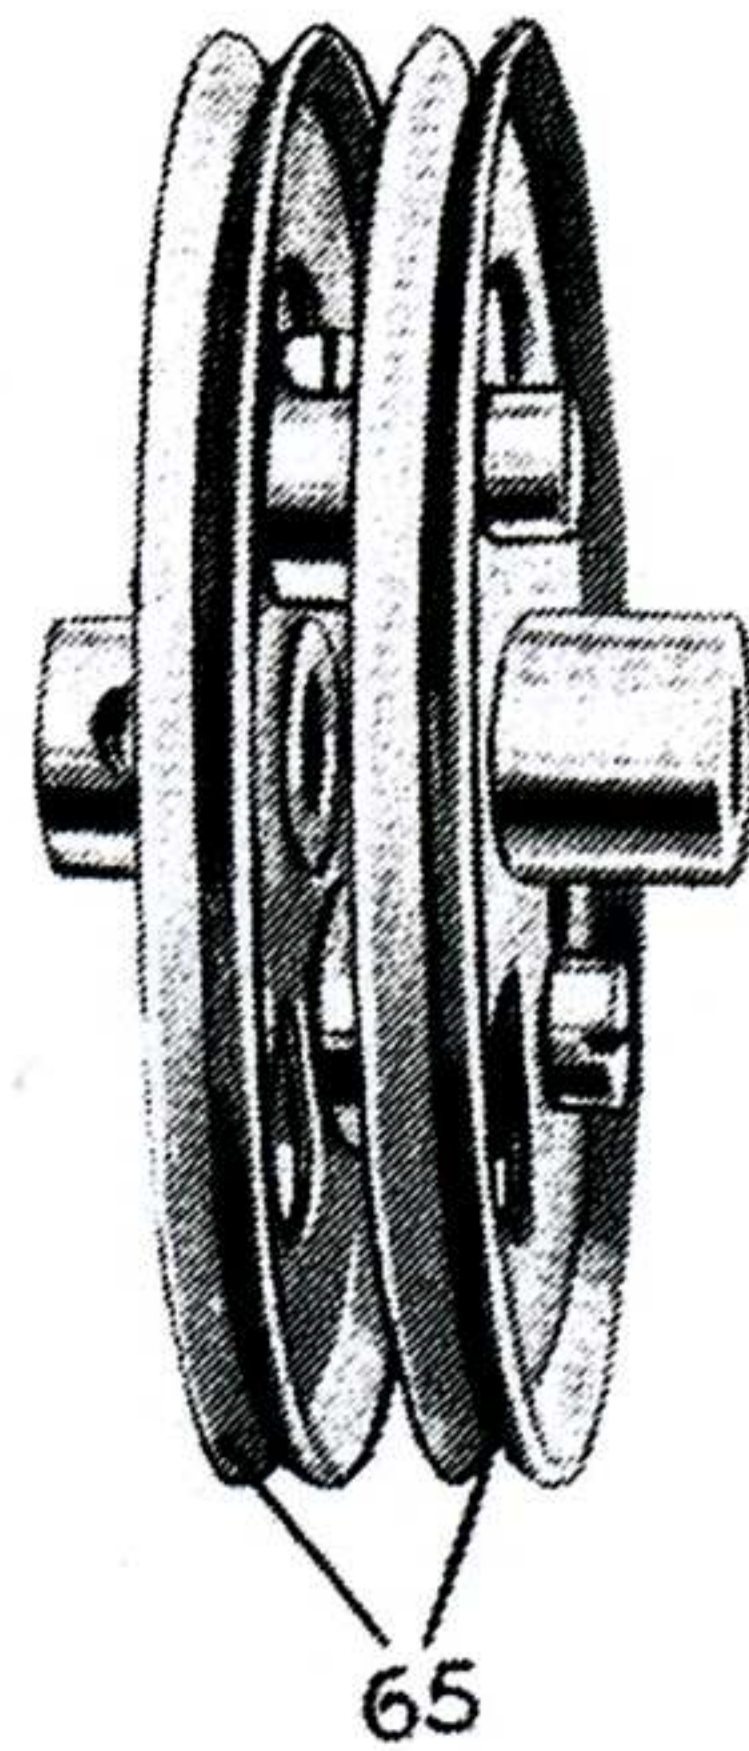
Roue d'atterrissage; le pneu est enlevé
